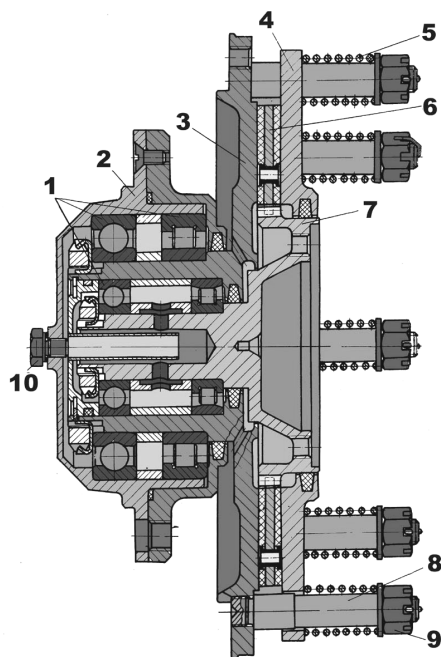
Фрикцион вентилятора: 1 – подшипники фрикциона; 2 – корпус подшипника; 3 – ведомая ступица; 4 – нажимной диск; 5 – пружины; 6 – диск трения; 7 – ведущая ступица; 8 – шпилька; 9 – гайка; 10 – пробка
